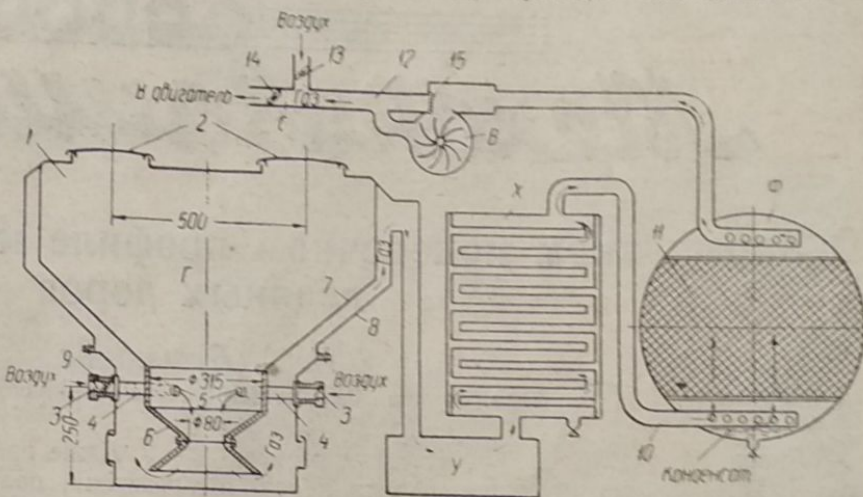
Схема газогенераторной установки Пельцера для автомобиля М-1
